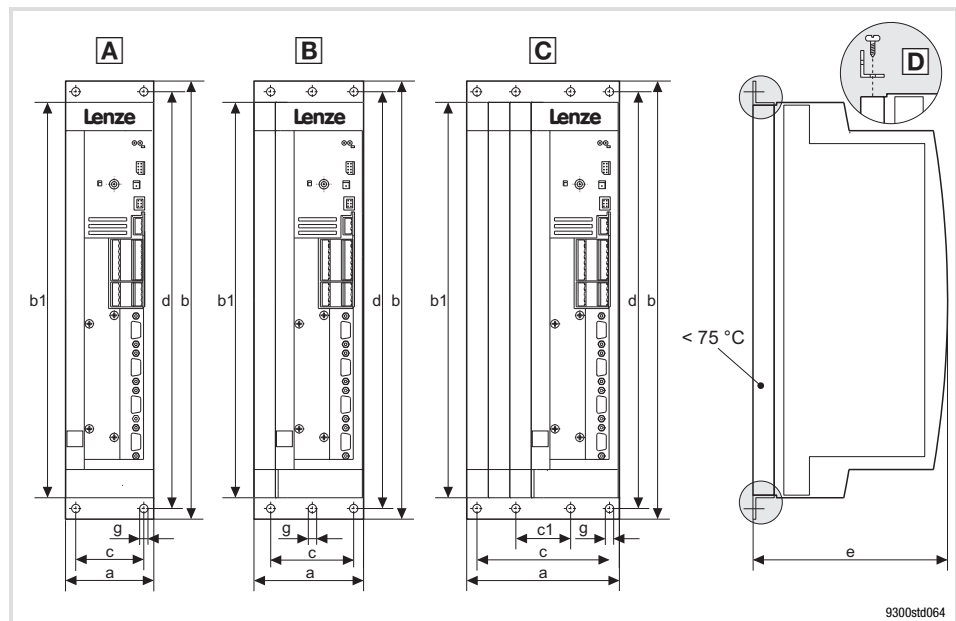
Abmessungen Montage in "Cold Plate"-Technik 0,37 ... 11 kW
